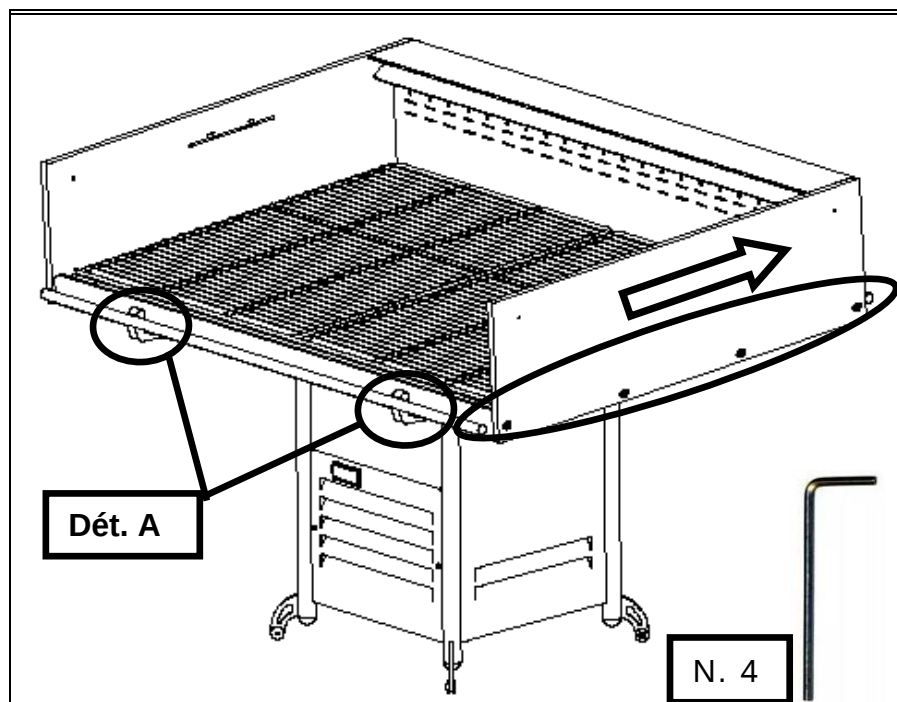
MEUBLE ARRIÈRE; enlèvement des pièces
